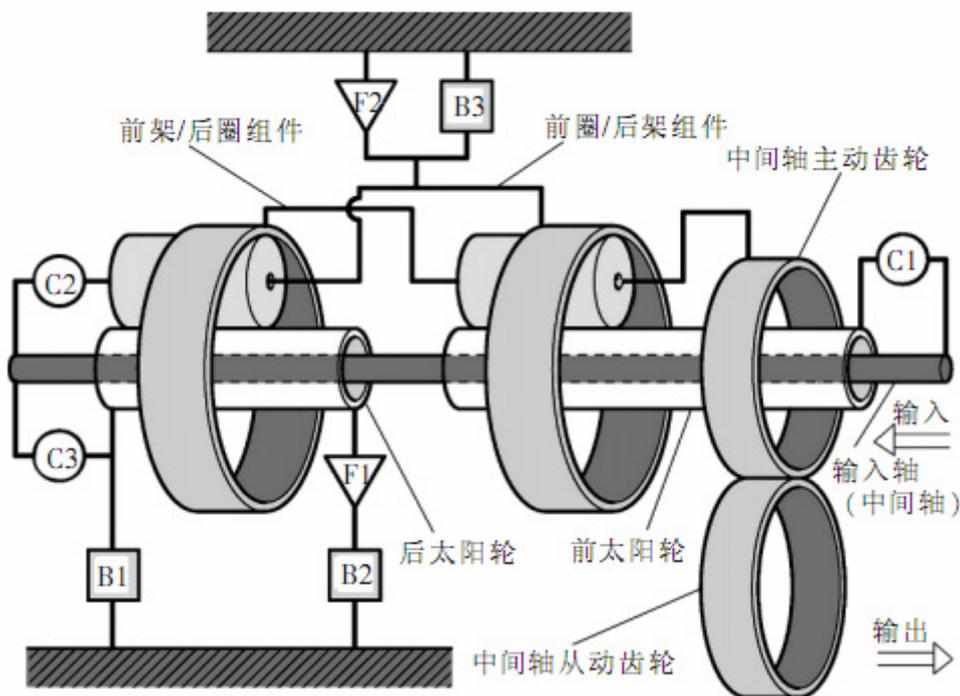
U341E 型自动变速器行星齿轮变速机构结构简图
